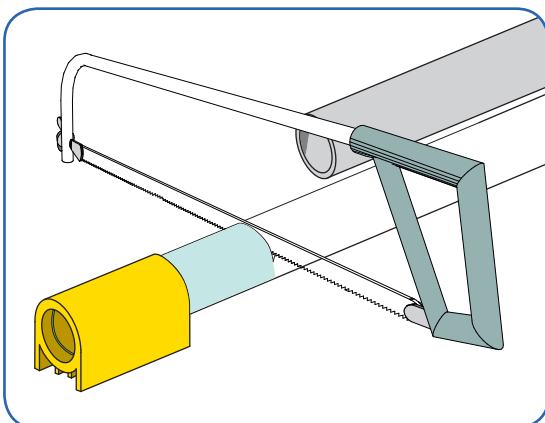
Cortando el tubo para montar el Kit final de línea.
